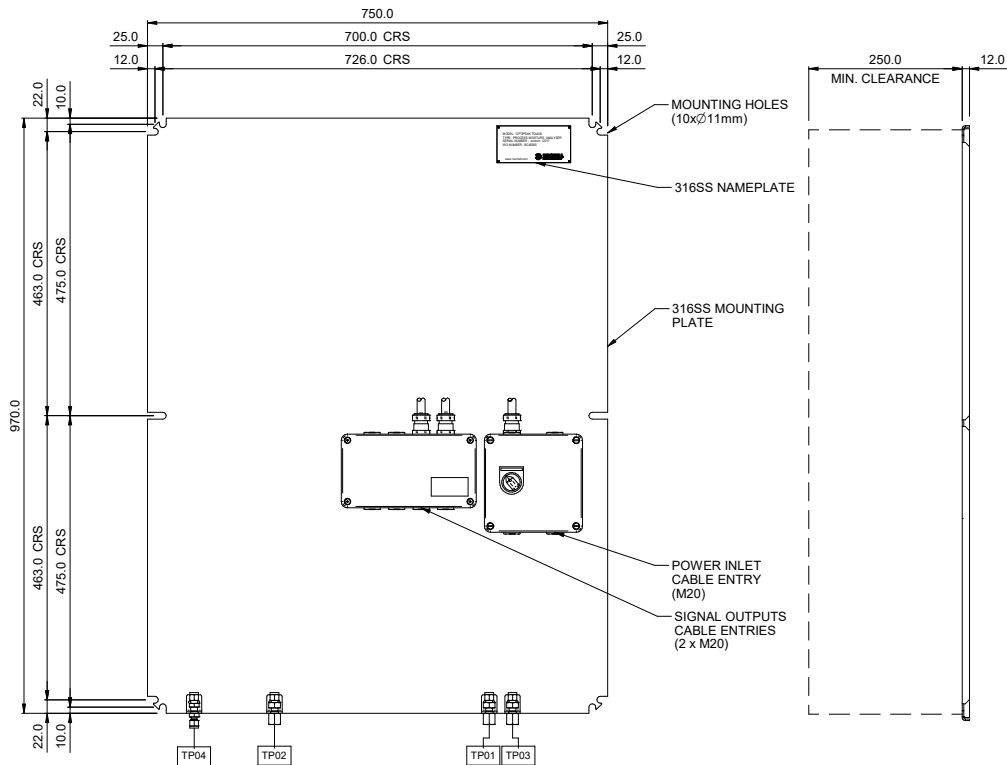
Maßzeichnung – Montageplatte für Innenaufstellung
